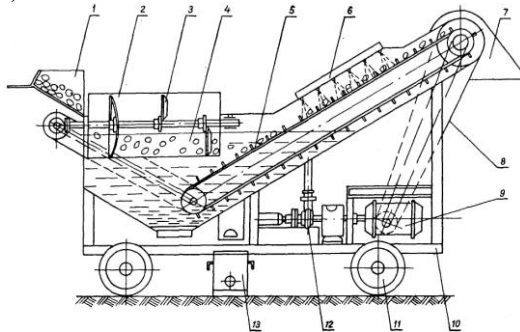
Машина для мийки плодів томатів МПП-1,5: 1 – завантажувальний лоток; 2 – мийний барабан; 3 – лопаті; 4 – ванна; 5 – вивантажувальний транспортер плодів; 6 – душовий пристрій; 7 – кожух; 8 – привід транспортера плодів; 9 – редуктор; 10 – рама; 11 – ходові колеса; 12 – насос подачі води в душовий пристрій; 13 – збірник насіння
